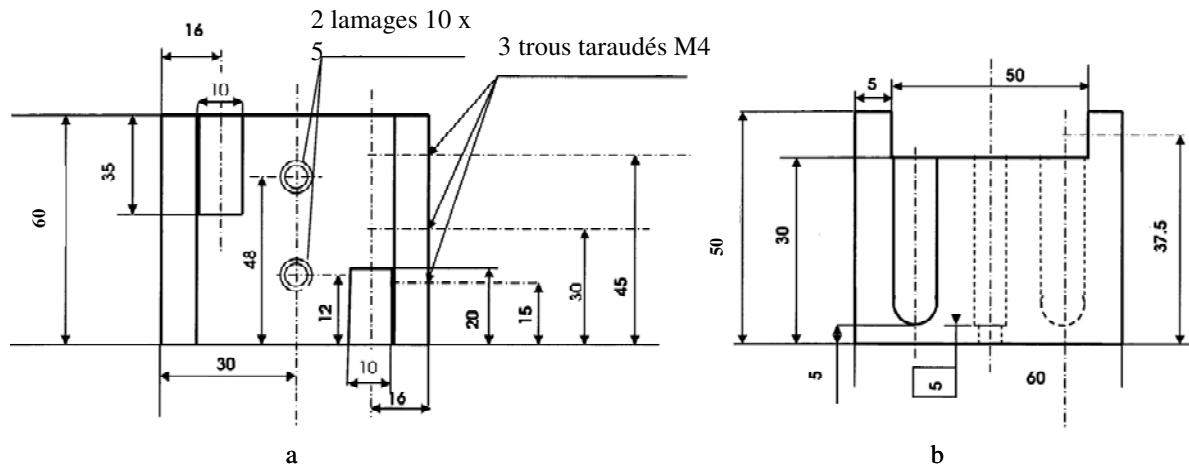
Dimensions de la pièce support (Fig. 2.18) vue de dessus (a) et vue de côté (b)
